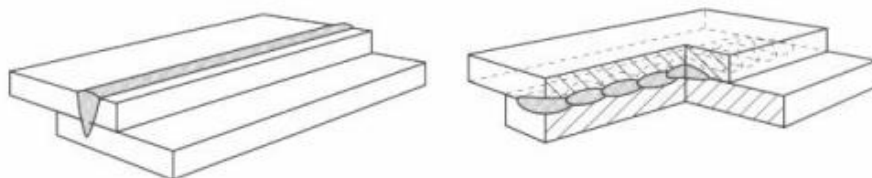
Izquierda: Costura de soldadura por haz de electrones; derecha: soldadura por costura.
